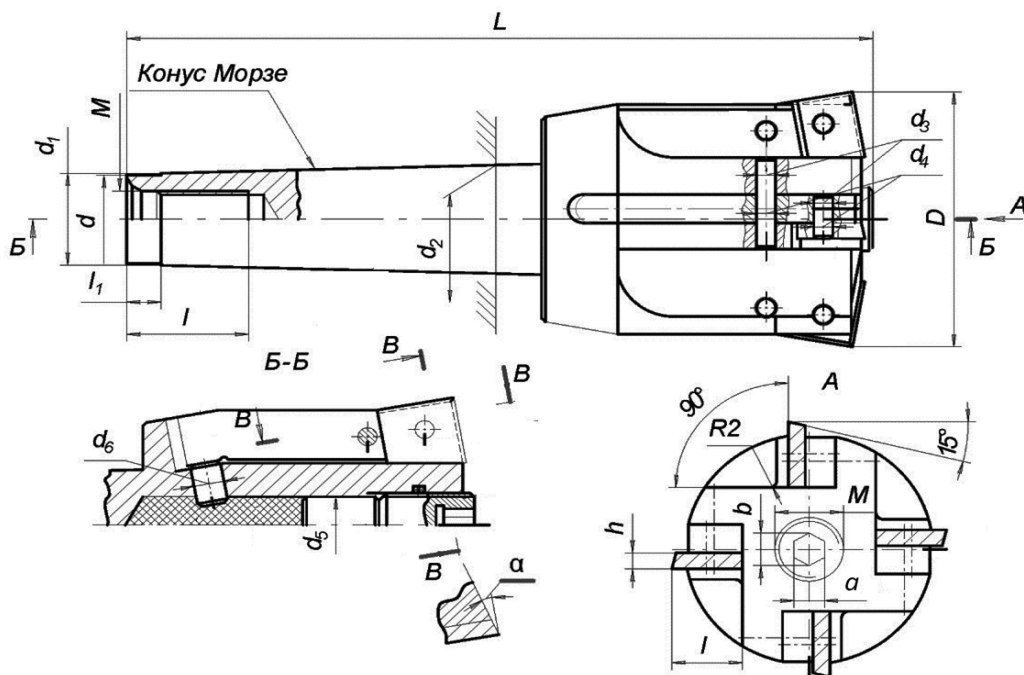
Зенкер хвостовий, оснащений твердосплавними пластинами
